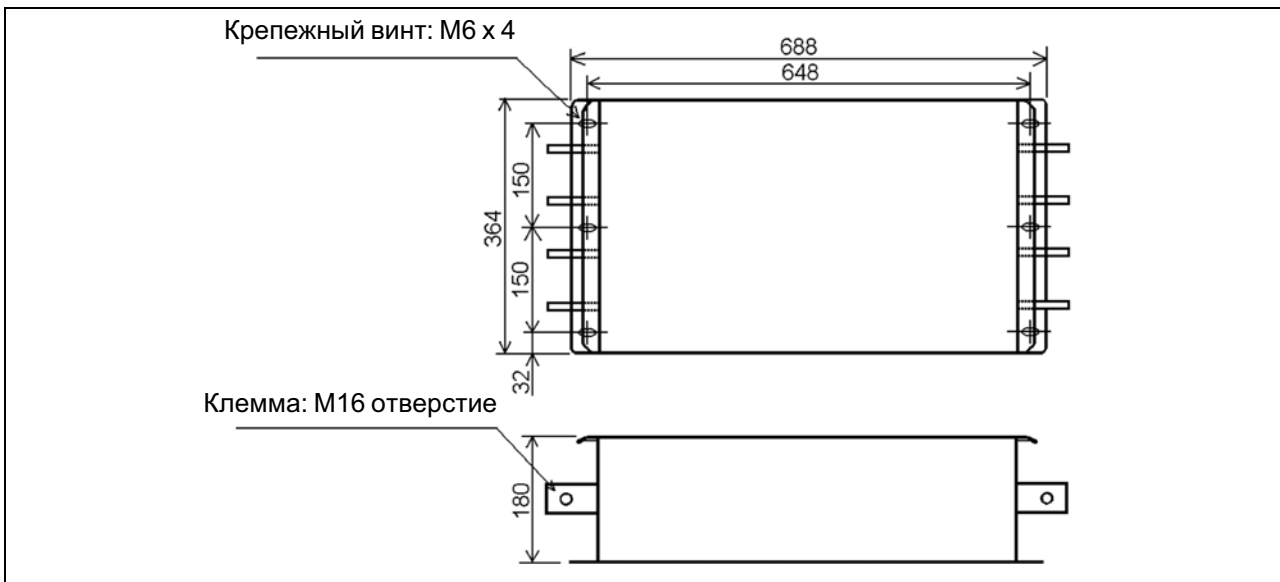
Габаритные размеры (RF3880-F11)
